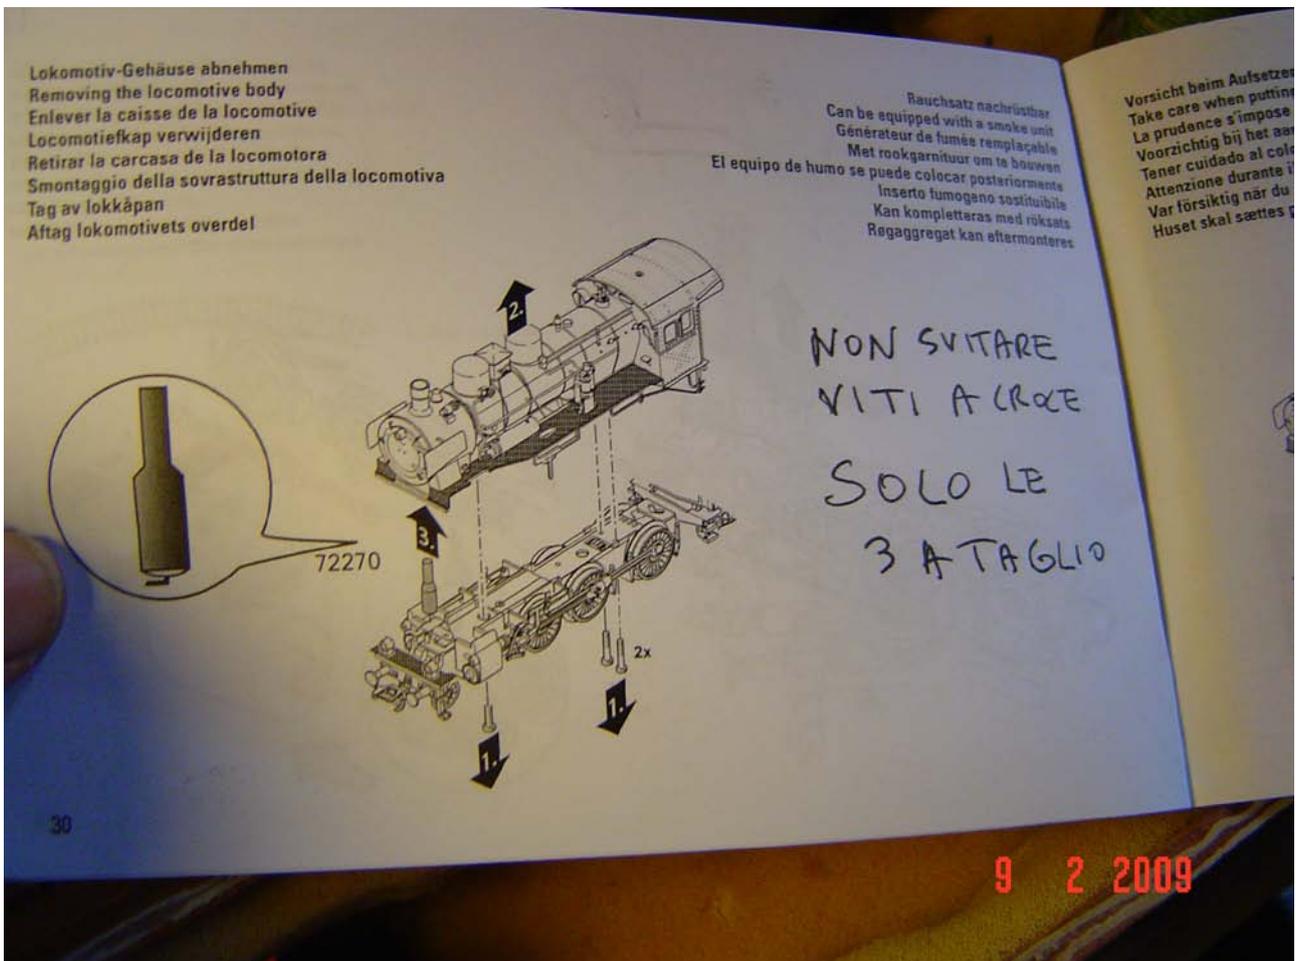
nel libretto d'istruzioni aggiungete questo semplice avviso!
